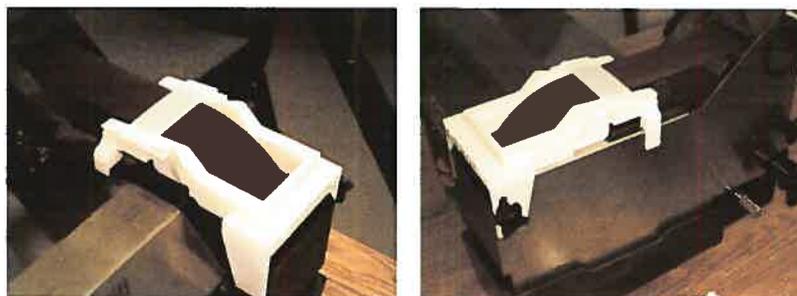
Deuxième Prototype sur la machine à l'UQAM. ¹⁵⁶
